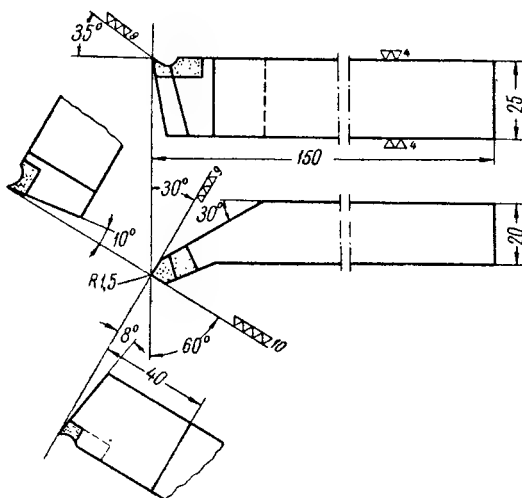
Резец с твердосплавной пластиной ВК8 для чистового обтачивания коллекторов
